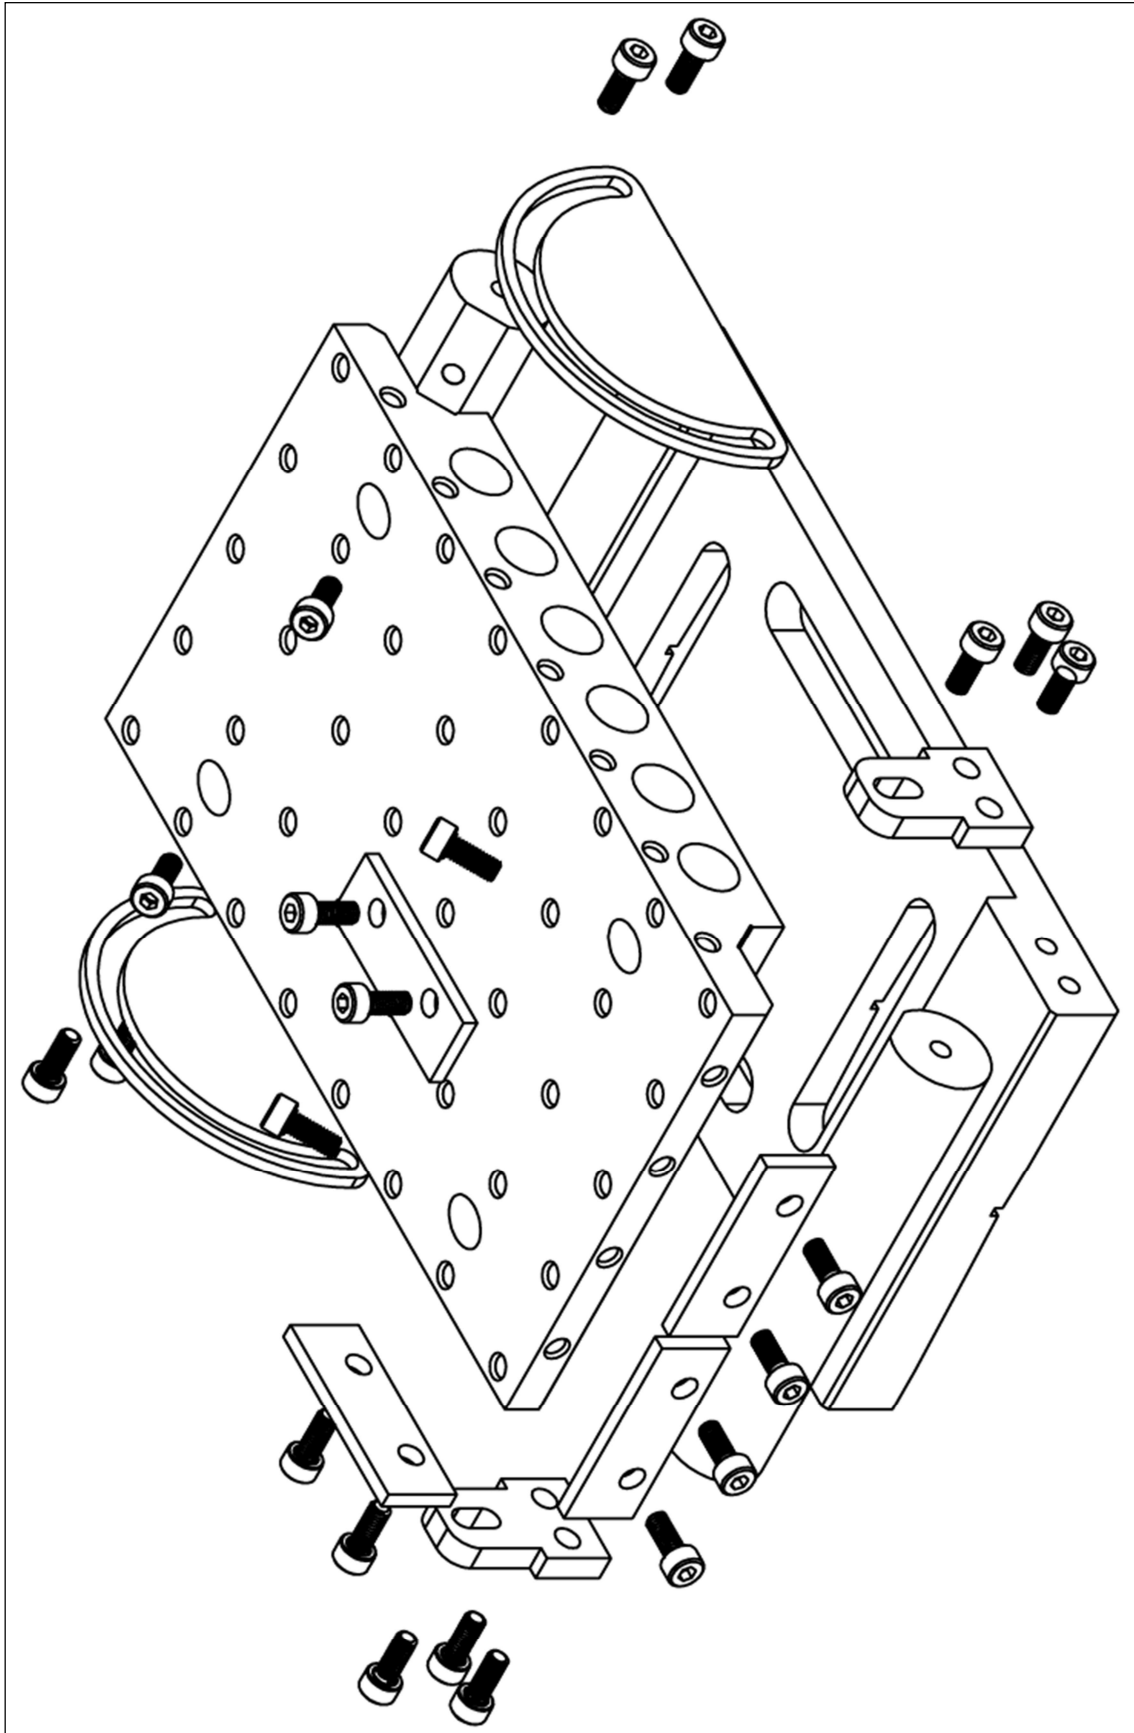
Desenho 3D de conceito do equipamento para medição angular com acessórios para usinagem.
